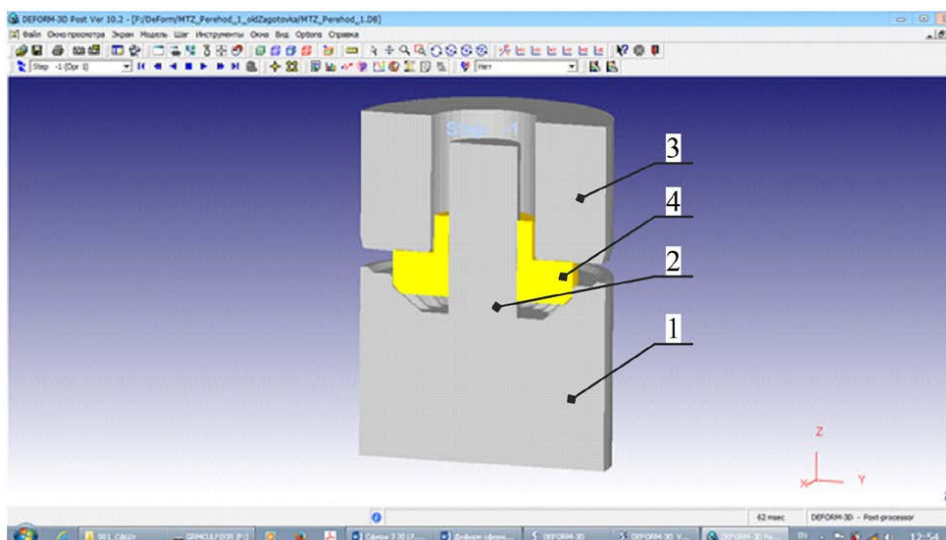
3D-модель инструмента и заготовки для первого перехода штамповки конического зубчатого колеса
